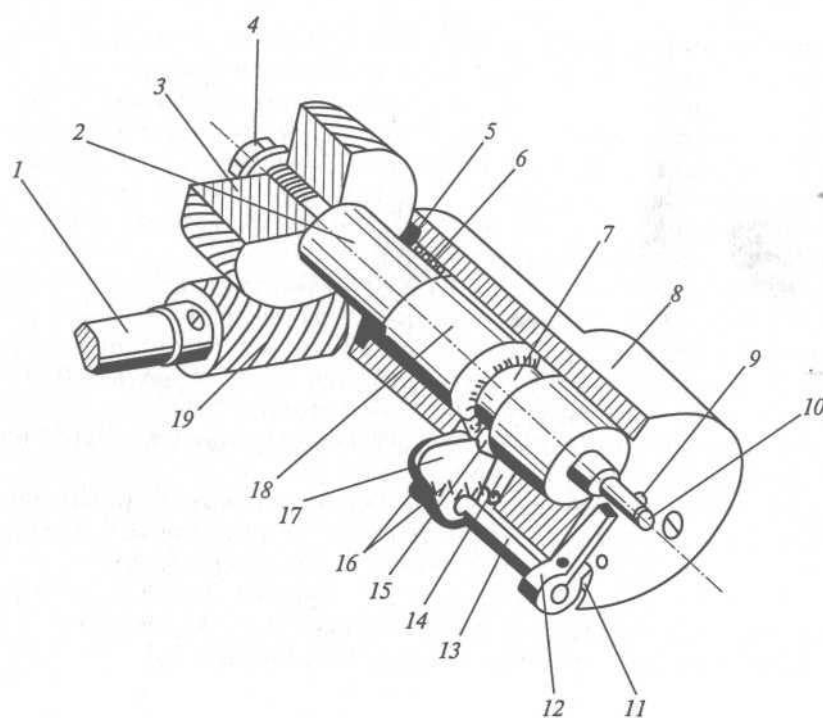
Схема пристрою для намотки нитки на шпульку в машині 1022М
